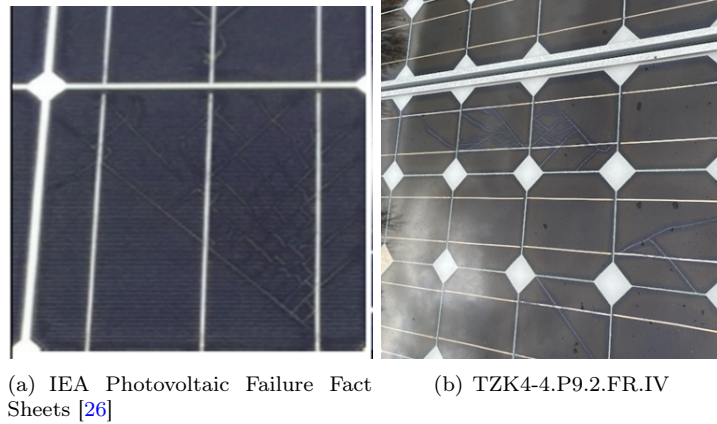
Fisura múltiple en celdas o snail track
